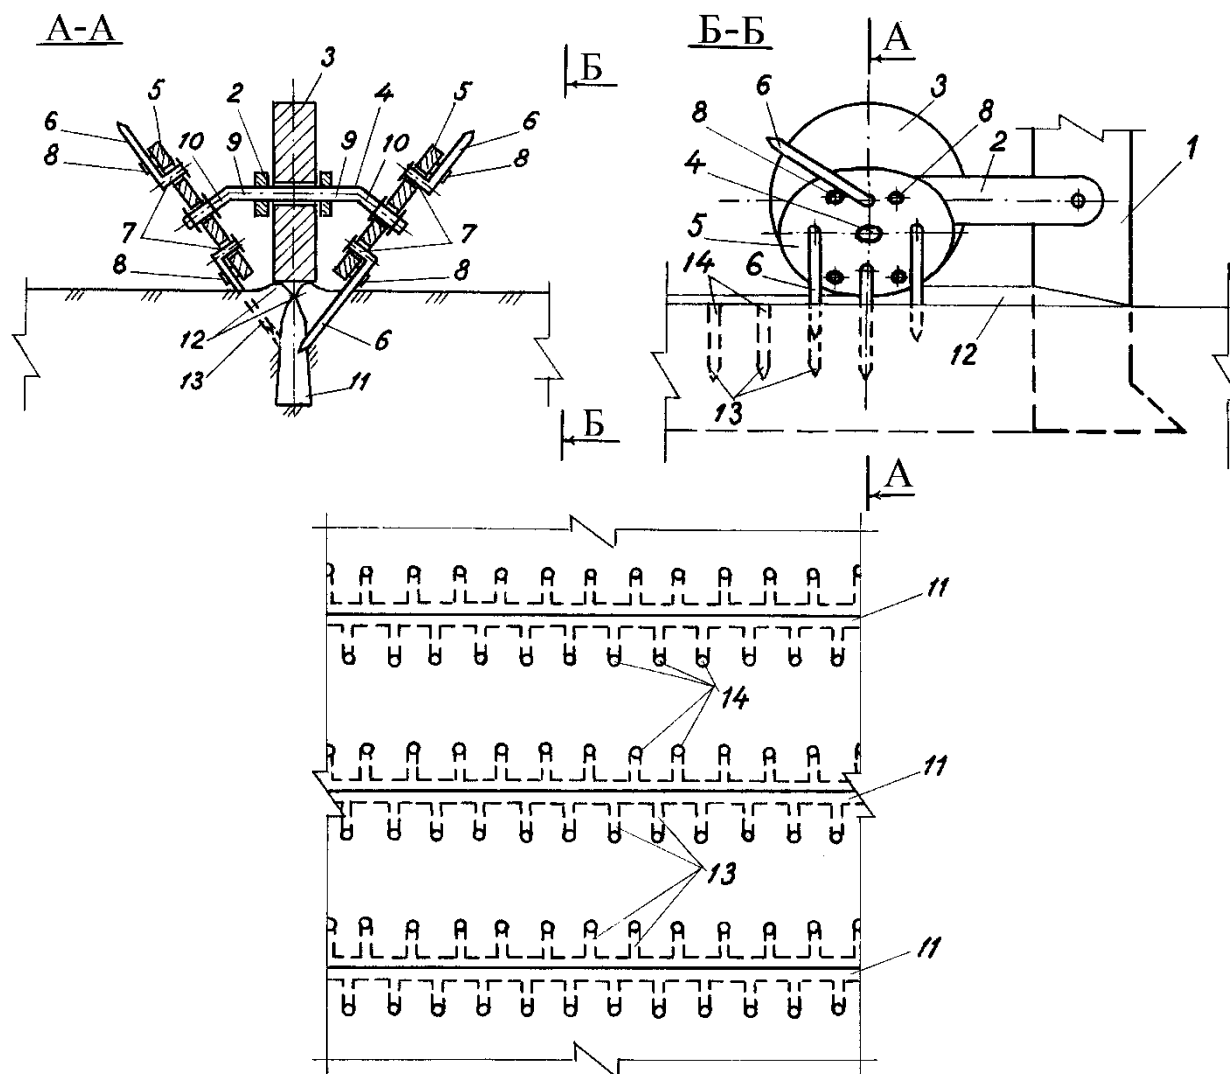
Принципиальная схема устройства для обработки поверхности поля [6]: 1 – рабочий орган щелереза; 2 – кронштейн; 3 – прикатывающий каток; 4 – ось катка; 5 – штифтовальный диск; 6 – штифт; 7 – шарнир; 8 – ограничитель; 9 – оси вращения прикатывающего катка; 10 – ось вращения штифтовальных дисков; 11 – щель в почве; 12 – почвенный валик; 13 – вертикальные отверстия в почве
